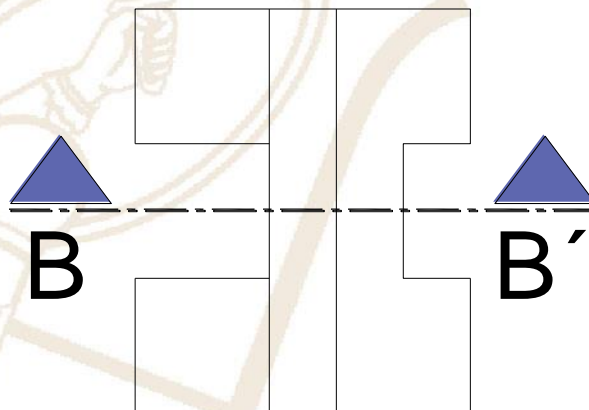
Vista en planta del objeto señalando el eje de plano de corte.
